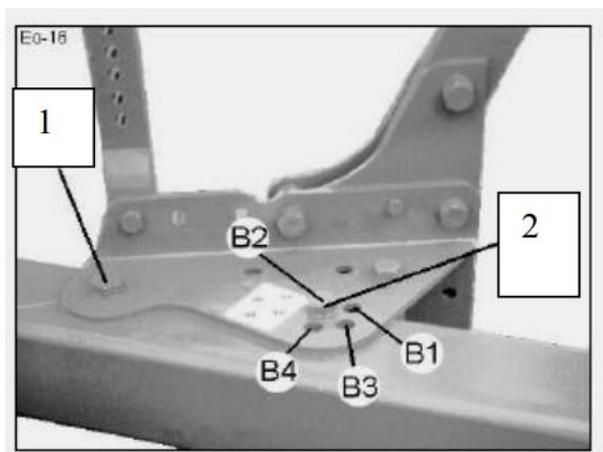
Установка ширины захвата каждого корпуса по схеме перестановки (позиции В1-В4): *1* – центральный винт; *2* – регулировочный винт
